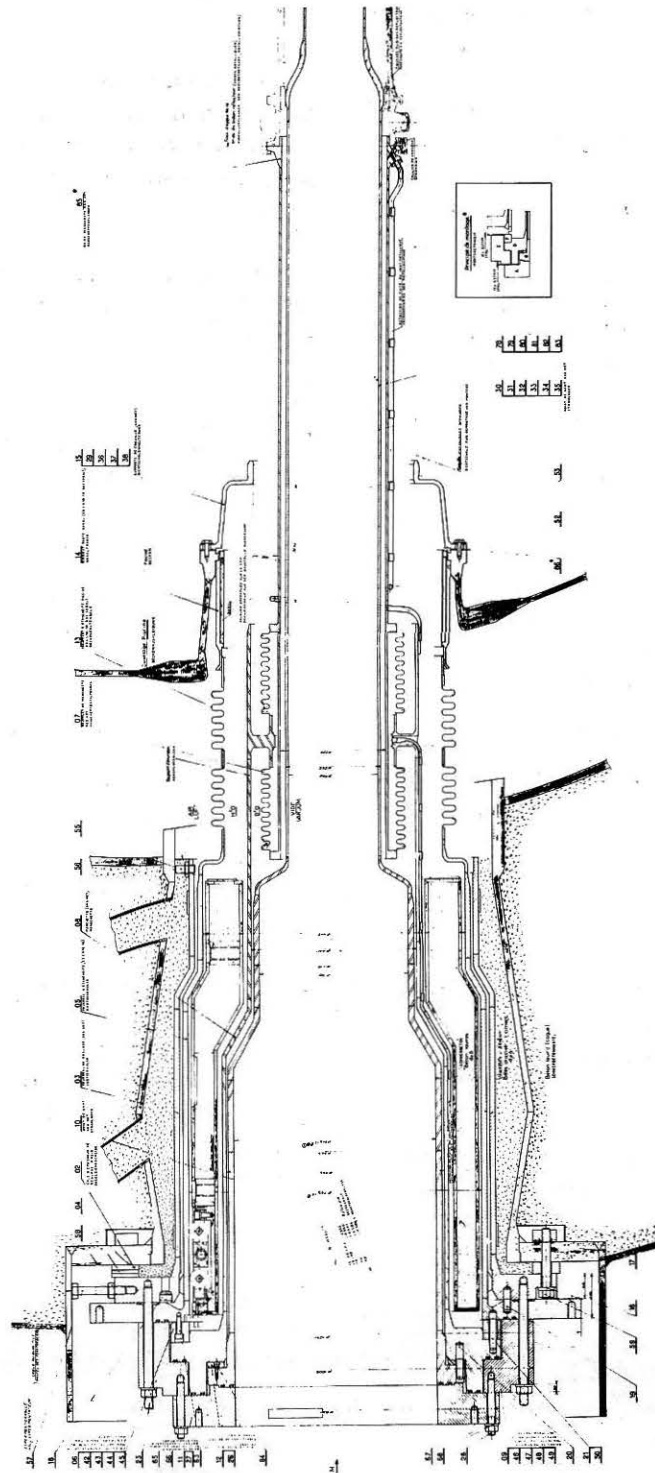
Canaux horizontaux. Coupe longitudinale.
